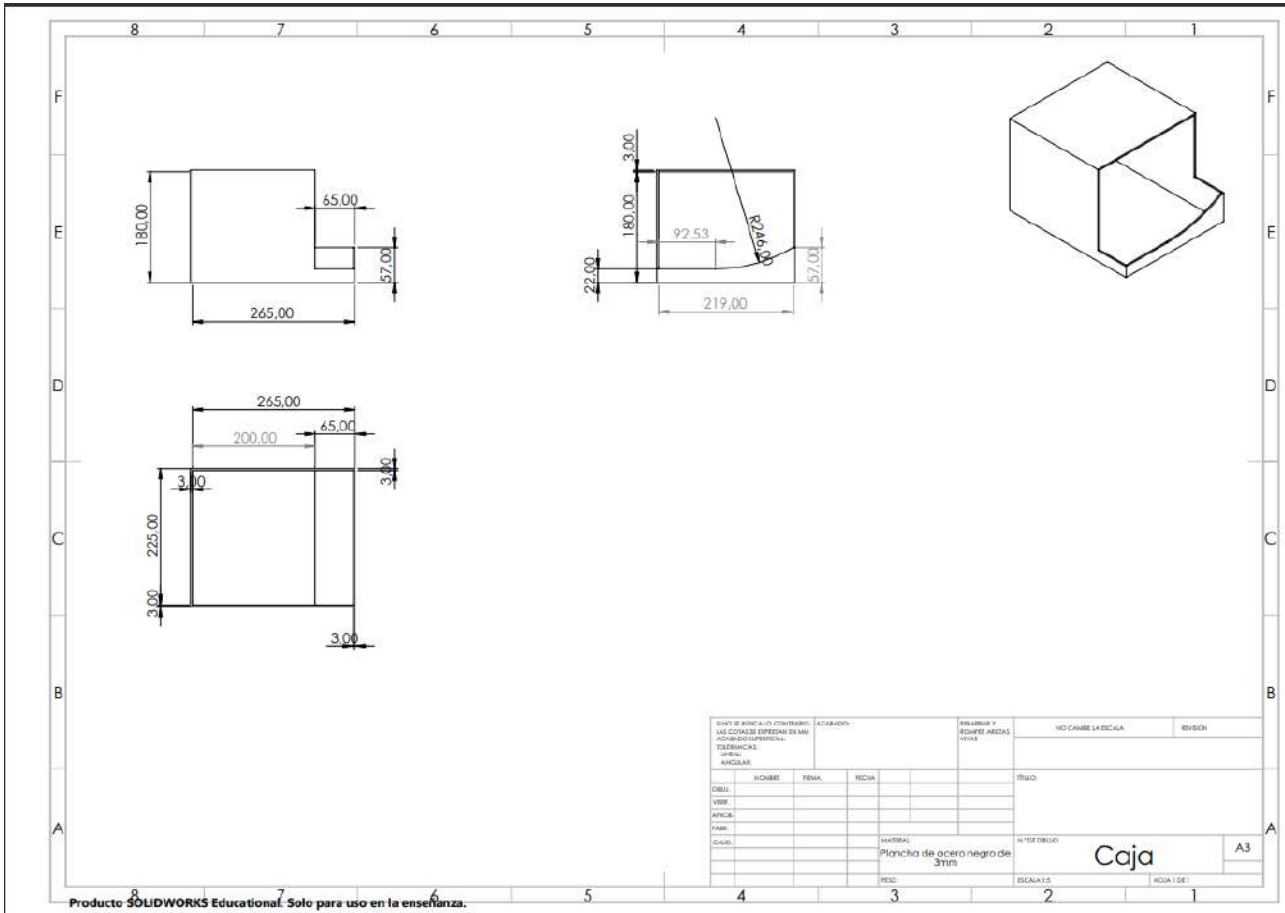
Caja base de la aspirado diseñada y acotada, por J. Bayas, SolidWorks
